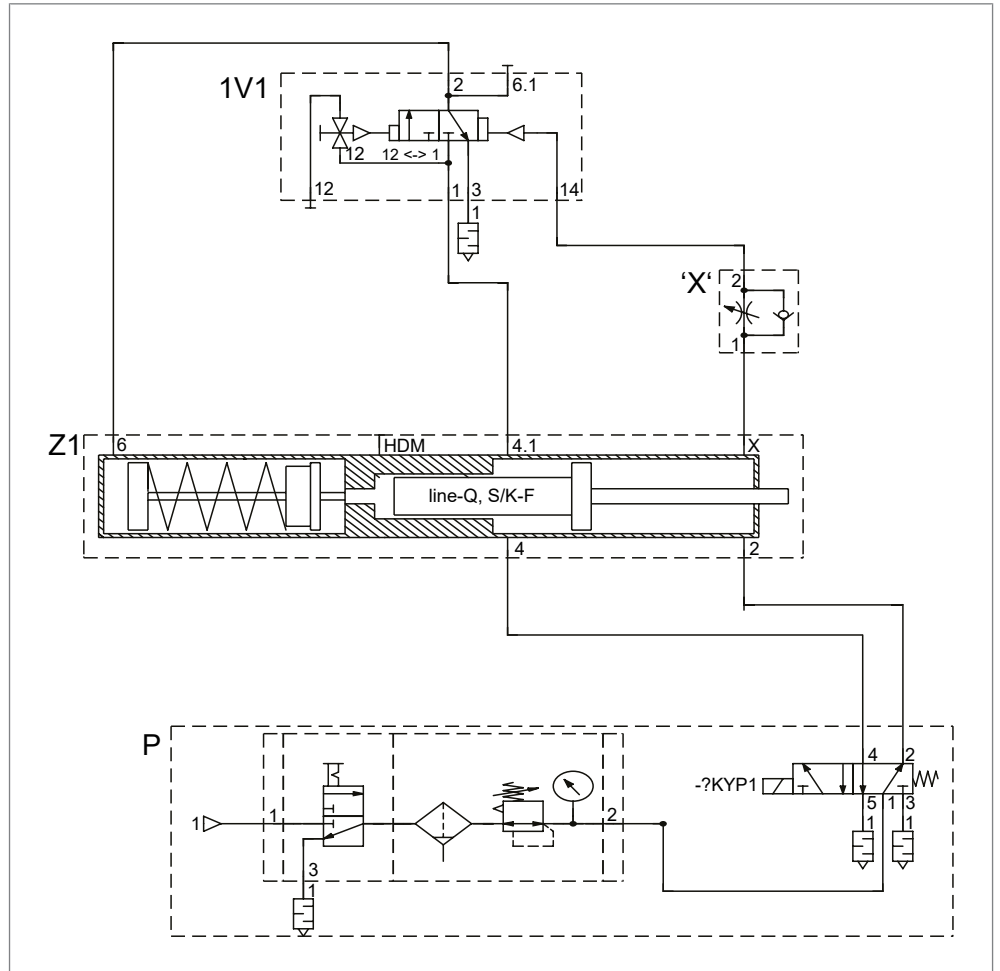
Ansteuerung nach Staudruckverfahren für Kraftpaket mit mechanischer Feder
